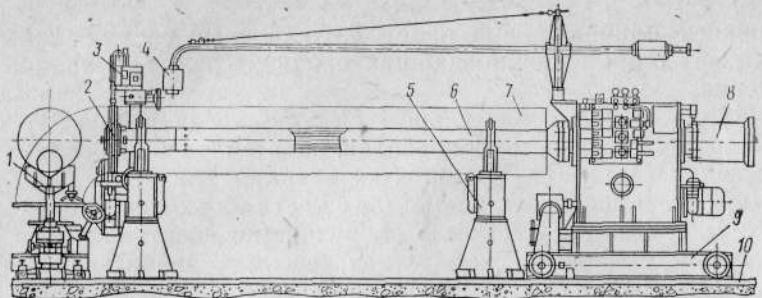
Установка для сборки и автоматической сварки плоских узлов трубопроводов с  $D_y = 200\ldots 500$  мм с внутренним силовым центратором
